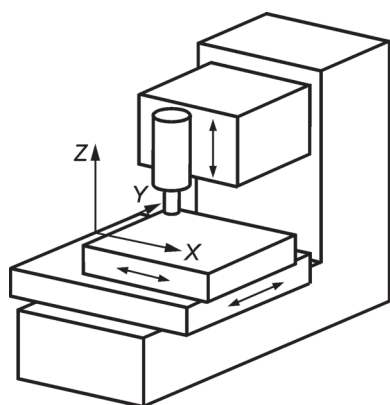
Схематическое изображение компоновки обрабатывающего центра Kondia A-10
